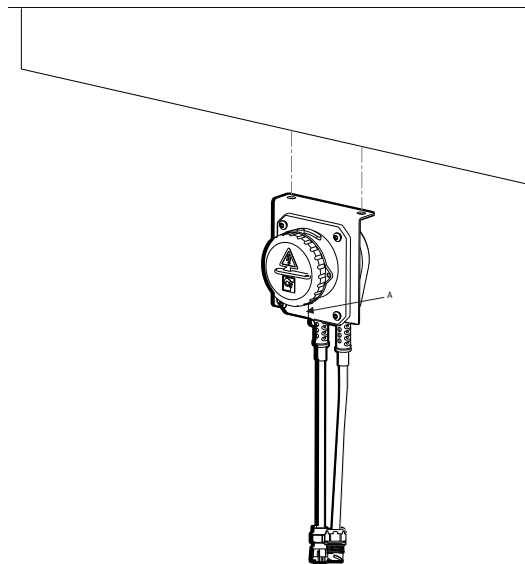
Montage des Hauptschalters. (Ablauf = A)
